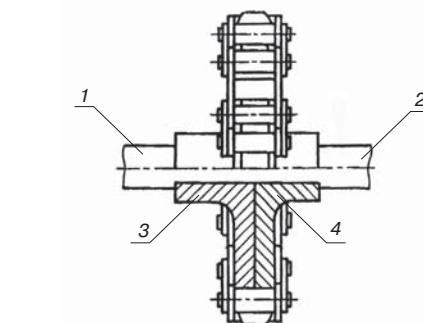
Цепная муфта: 1 – вал редуктора; 2 – вал смесителя; 3 – полузвездочка вала редуктора; 4 – полузвездочка вала смесителя; 5 – двоянная цепь
